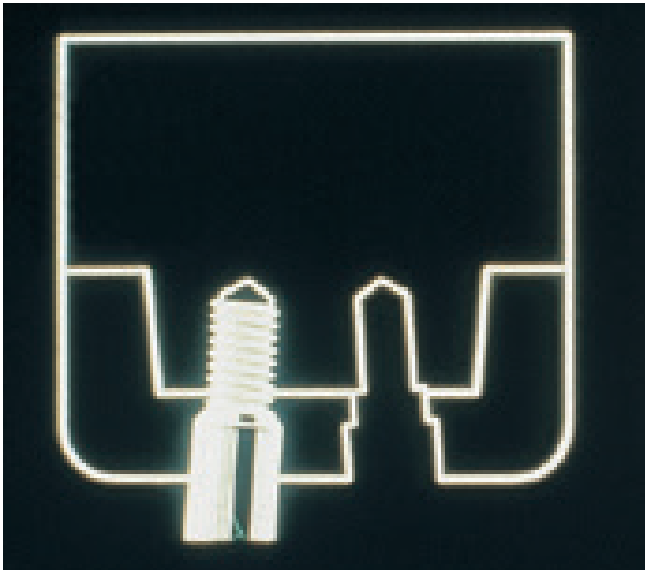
Prinzip der Versenkschraube (technische Skizze)
